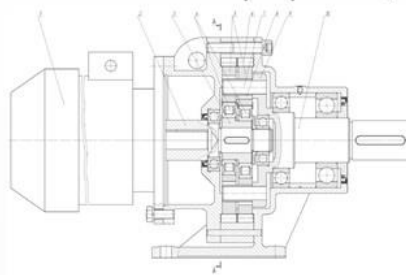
Конструкція планетарно-цивкового моторредуктора типу К-Н-В
